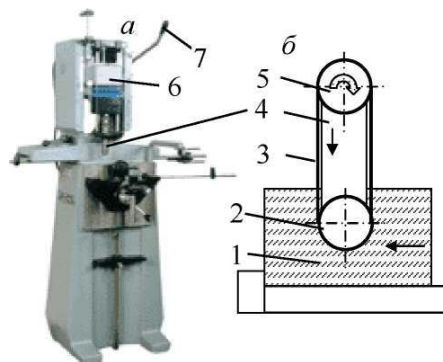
Верстат ланцюгово-довбальний: *а* - загальний вигляд; *б* - схема обробки паза
